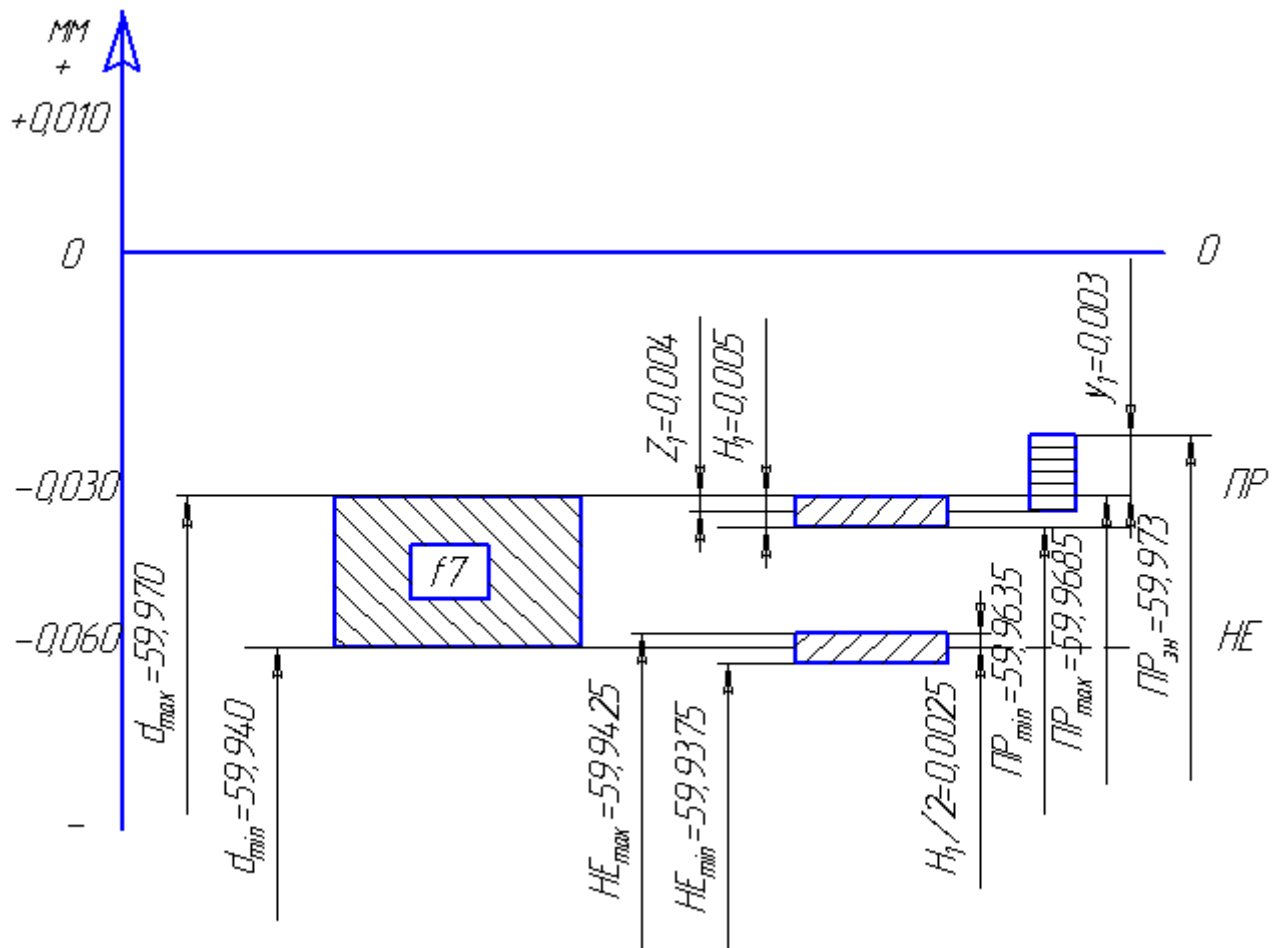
Схема розміщення полів допусків на виготовлення калібру - скоби для контролю вала  $\varnothing 60f7$
